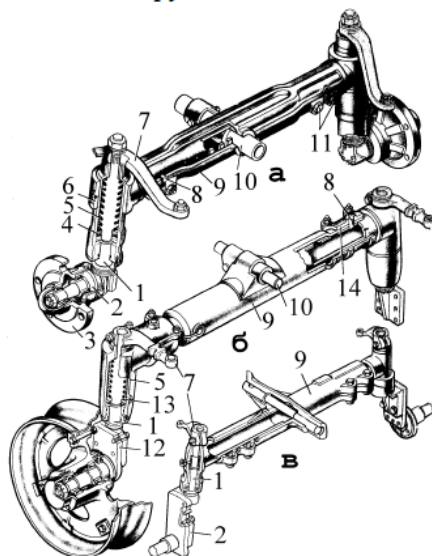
Передние мосты пропашных тракторов с эластичной (а и б) и жесткой (в) подвеской: 1 – поворотная цапфа; 2 – ос поворотной цапфы; 3 – ступица колеса; 4 – опорный подшипник; 5 – пружина; 6 – выдвигной кулак; 7 – поворотный рычаг; 8 – штифт; 9 – корпус переднего моста; 10 – ось качания переднего моста относительно остова трактора; 11 – болты крепления выдвигного кулака; 12 – фланец составной цапфы; 13 – масленка; 14 – хомут крепления выдвигного кулака
